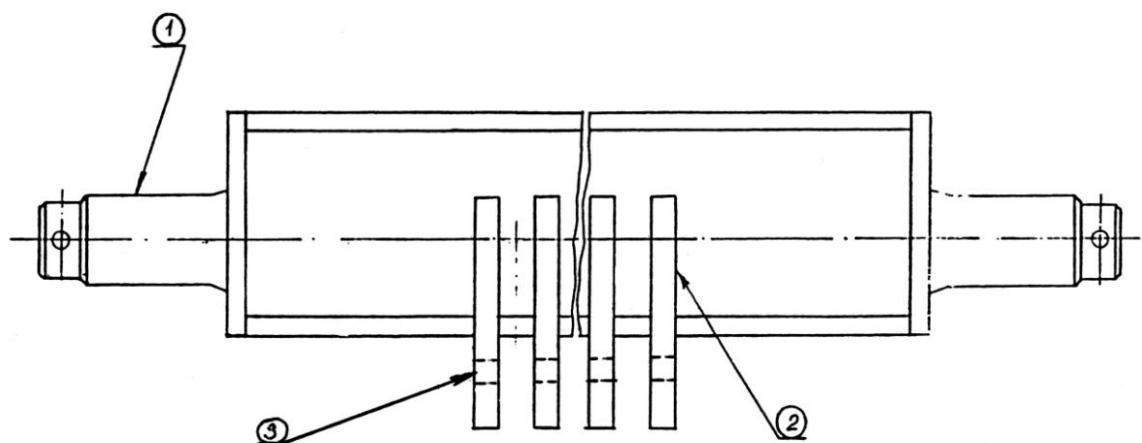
Дефекты траверсы, ремонтируемые сваркой или наплавкой
